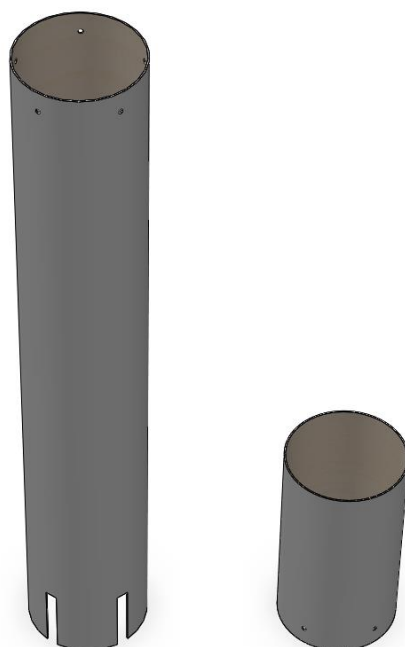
Modelo CAD del tubo principal (izquierda) y superior (derecha).
